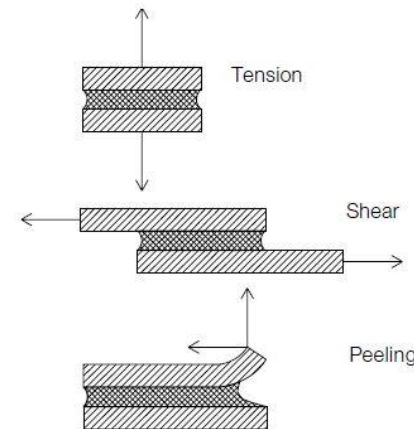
Cargas aplicadas a las uniones soldadas
